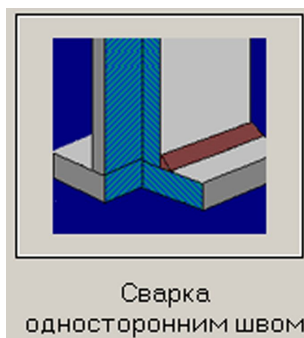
Выбор типа сварного соединения
